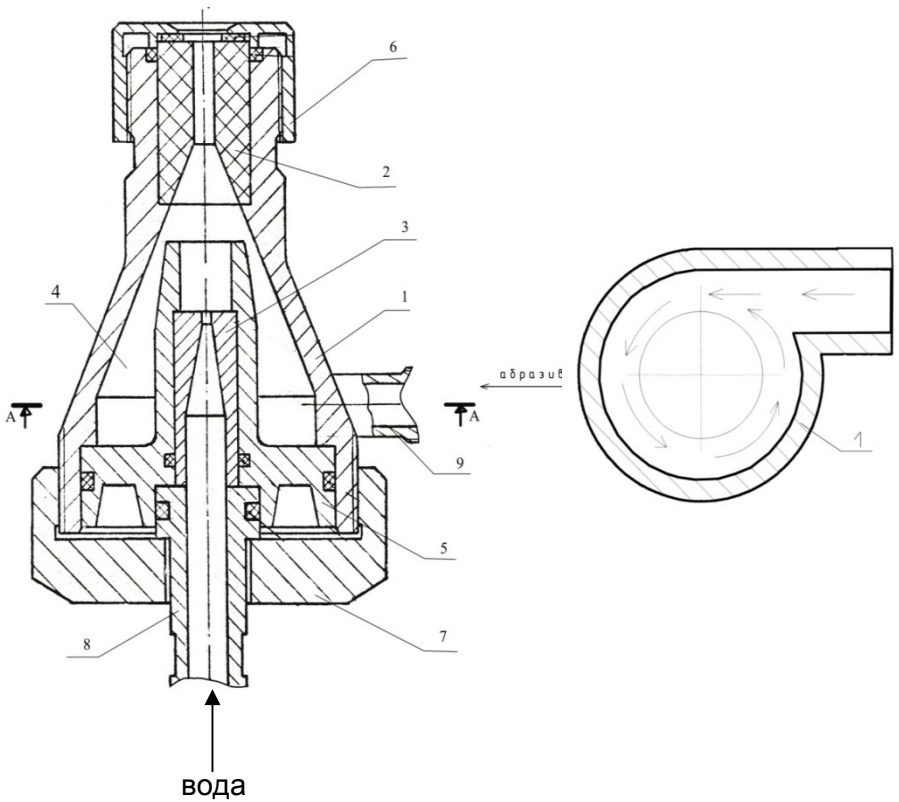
Схема пристрою для гідроабразивного очищення поверхонь
